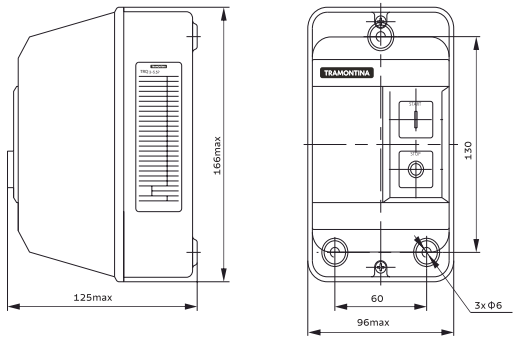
Starter Key Dimensions TRQ3 -5.5P
